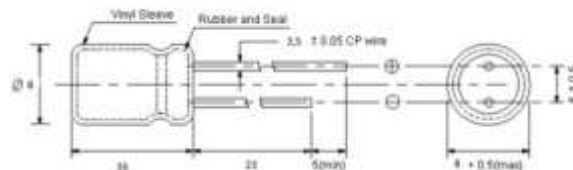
Габаритні розміри конденсатора типу ЕСАР
